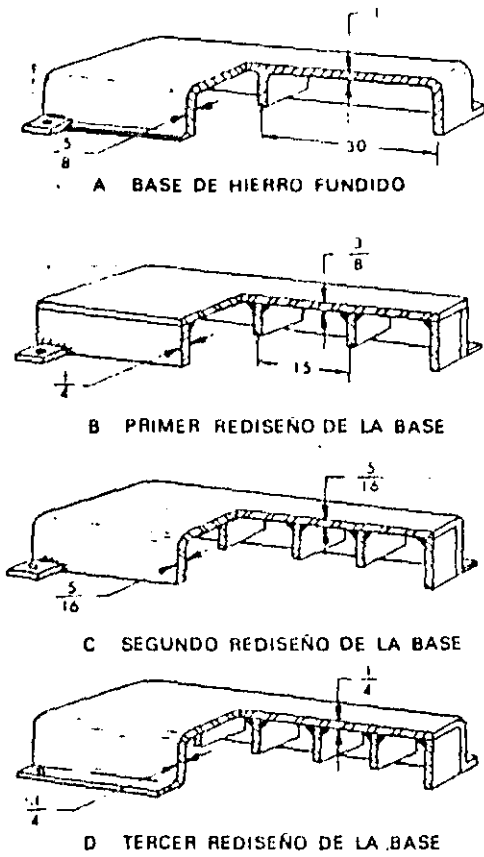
Base original de hierro fundido, rediseñada para fabricar en acero soldado
